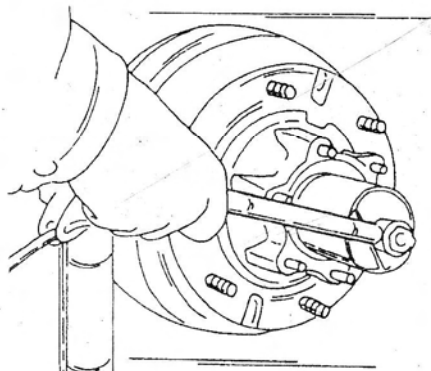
Отворачивание или заворачивание контргайки колесного подшипника специальным ключом.
